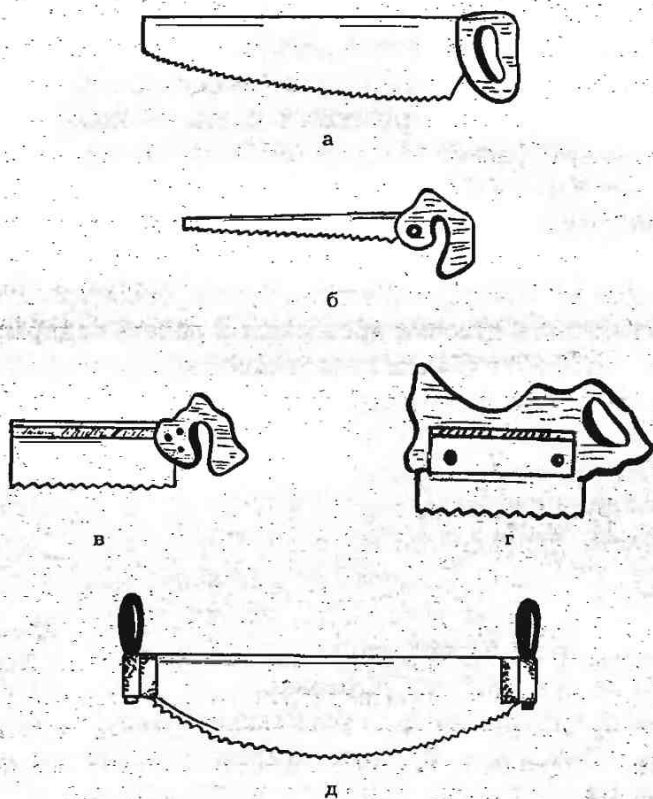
Виды ножовок: а — поперечная широкая; б — узкая; в — с обушком; г — ножовка-наградка; д — двуручная поперечная пила.
